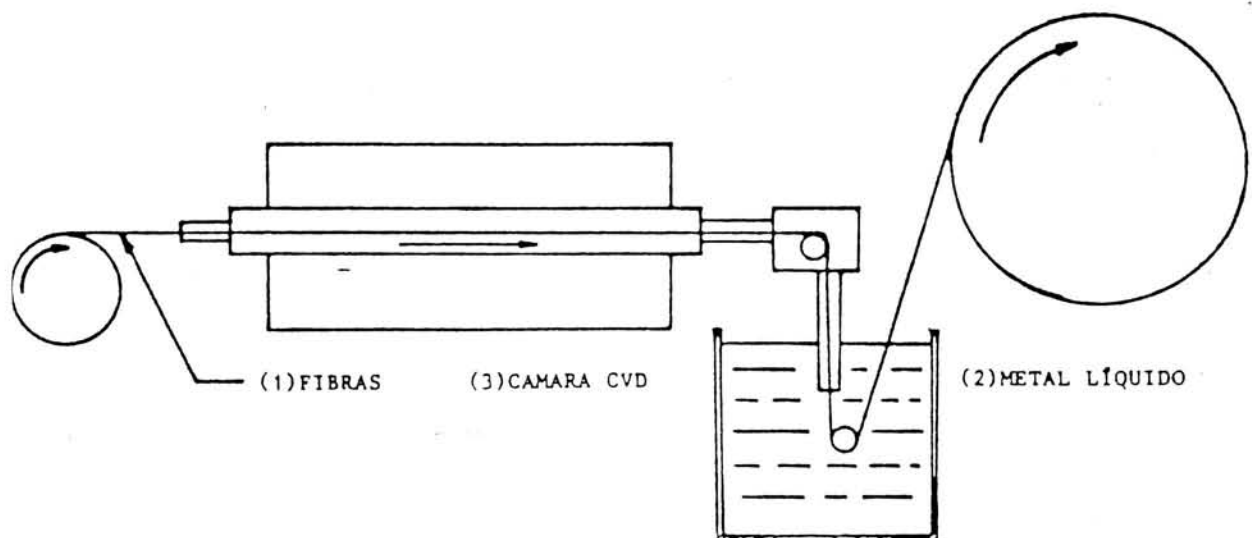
Equipamento em esquema, para a fabricação de "arame" de CMM [7]
